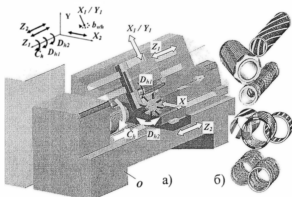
Вариант компоновки станка с ЦСФ (а) для получения среднегабаритных деталей (б)
